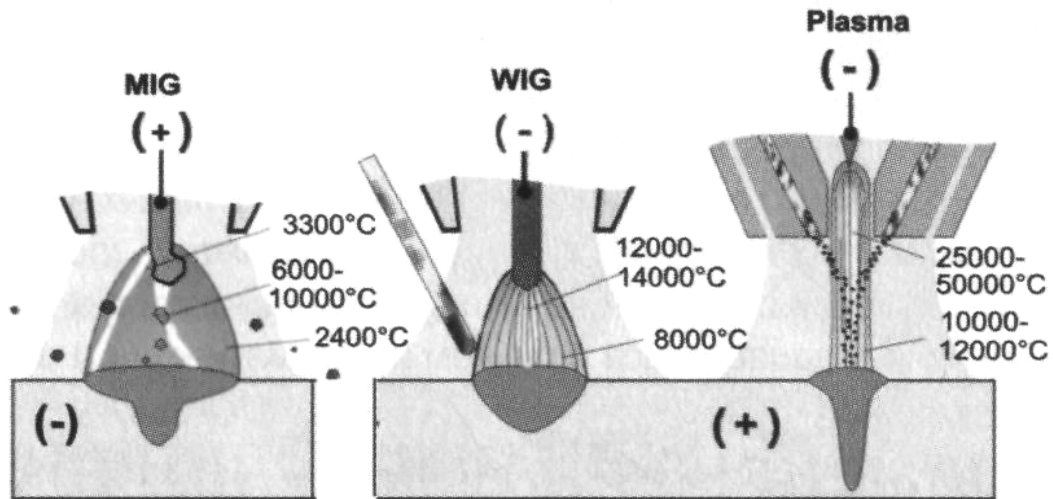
Отличительные особенности MIG/MAG, TIG и плазменного способов сварки.
